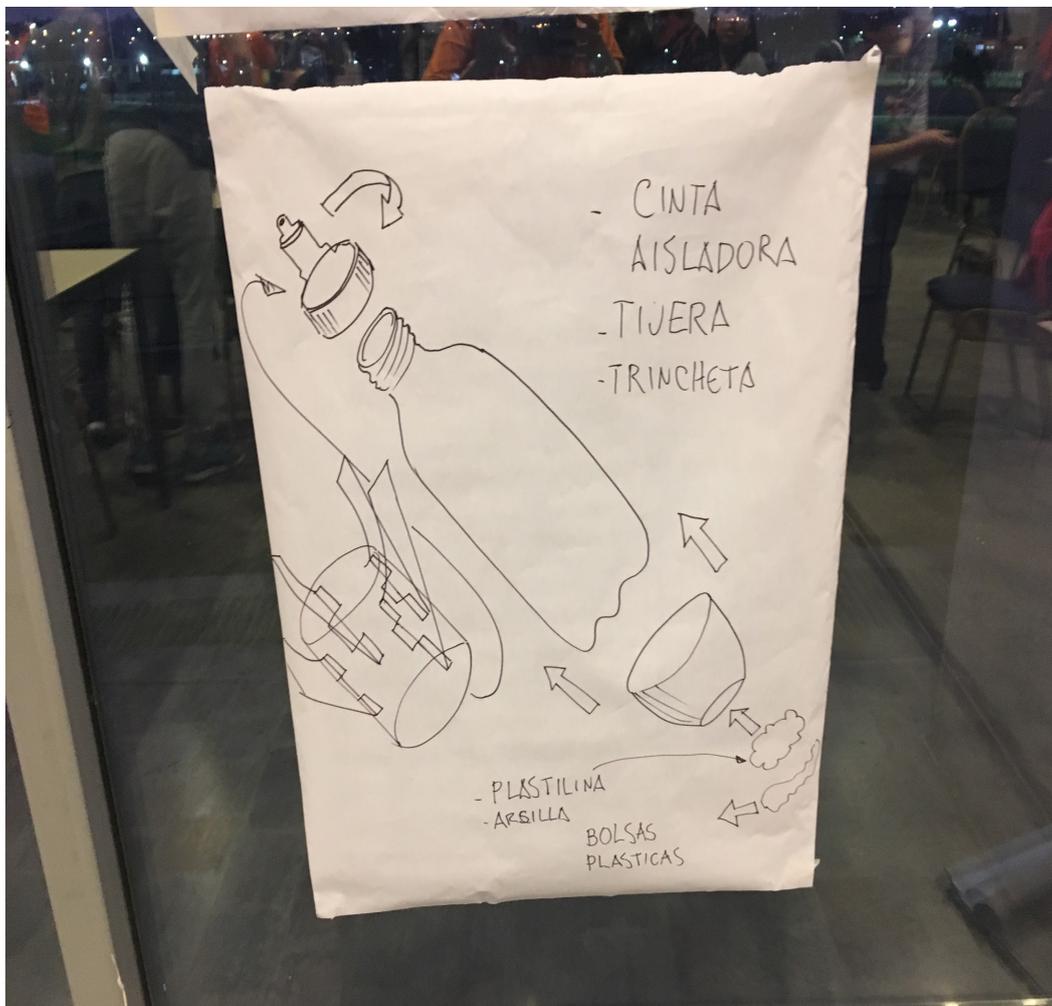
Despiece y ensamblado de la ojiva, la base y la tobera en el fuselaje.
